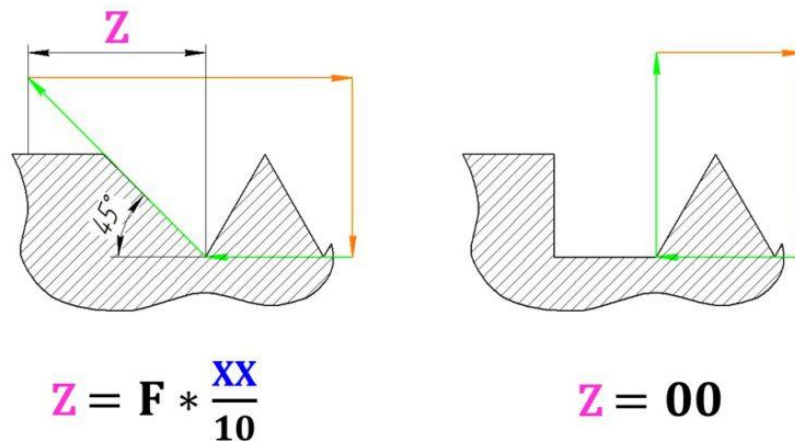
Розрахункова схема для визначення величини збігу різьби
